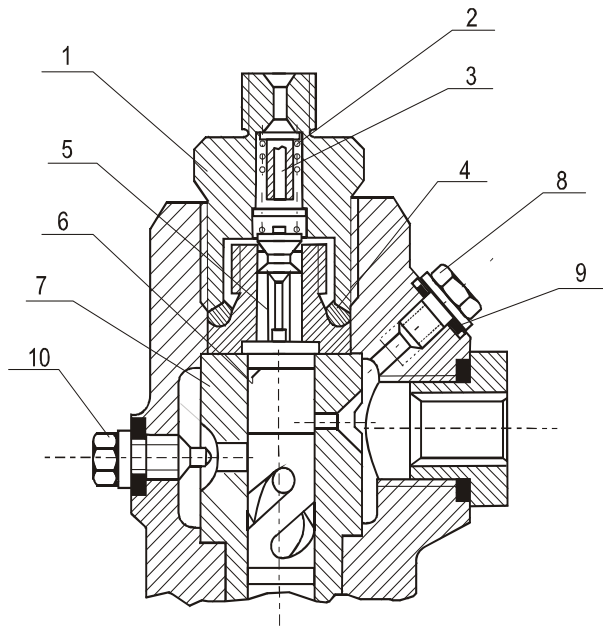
Топливный насос высокого давления: 1 — нажимной штуцер; 2 — пружина; 3 — ограничитель; 4 — уплотнительное кольцо; 5 — нагнетательный клапан; 6 — плунжер; 7 — втулка плунжера; 8 — пробка; 9 — прокладка; 10 — болт
